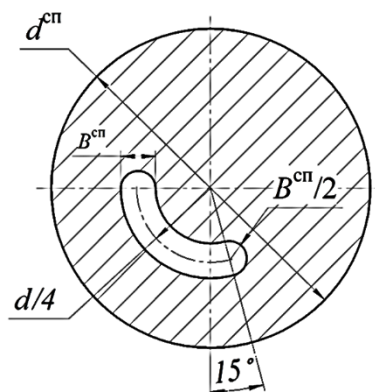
Форма поперечного сечения спечённой заготовки стебля РСТС
